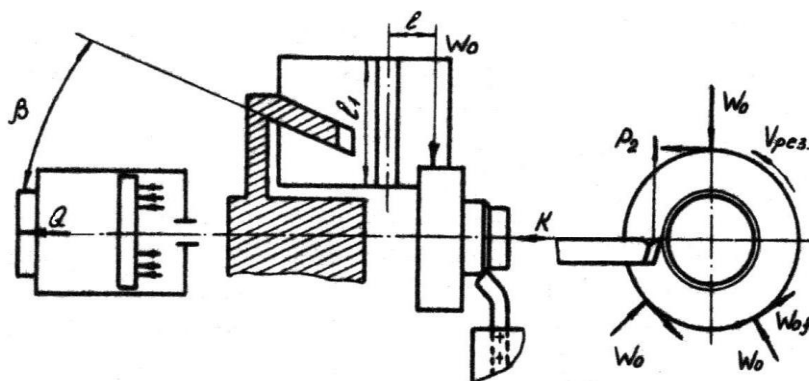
Схема установки і визначення зусилля затиску при обточуванні зовнішньої поверхні заготовки, яка закріплена в трьохкулачковому самоцентруючому патроні з механізованим приводом клинового типу
